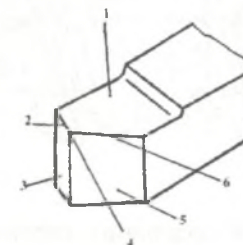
Рабочие поверхности и режущие кромки резца
